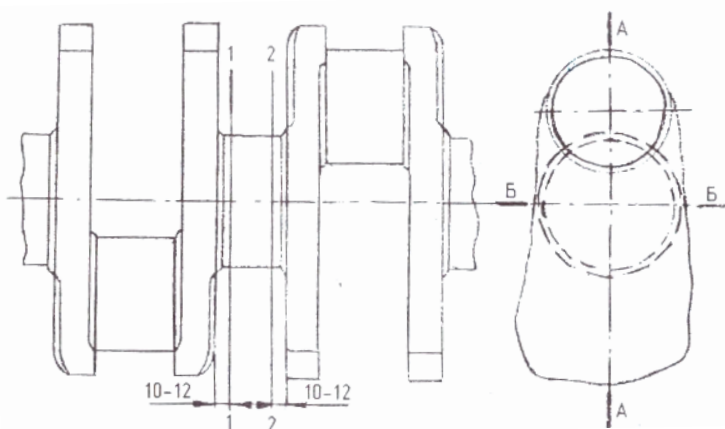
Схема измерений коренных шеек коленчатого вала
